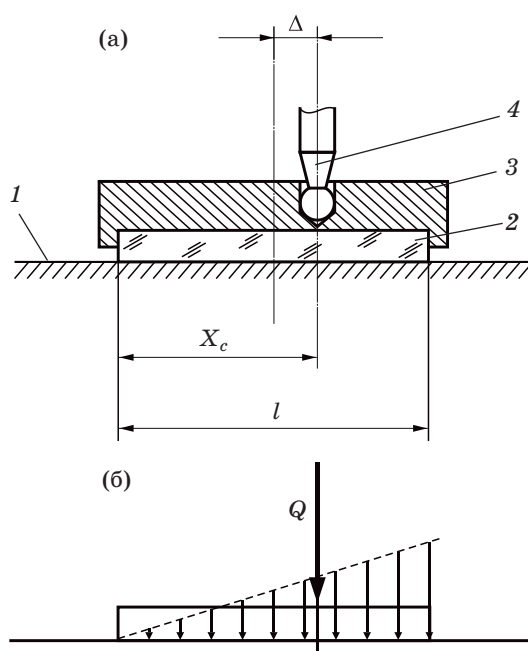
Приспособление, создающее неравномерно распределенную нагрузку на обрабатываемую поверхность ККЭ. а – схема приспособления: 1 – поверхность инструмента, 2 – ККЭ, 3 – прижим, 4 – поводок. б – эпюра распределения нагрузки по обрабатываемой поверхности.
